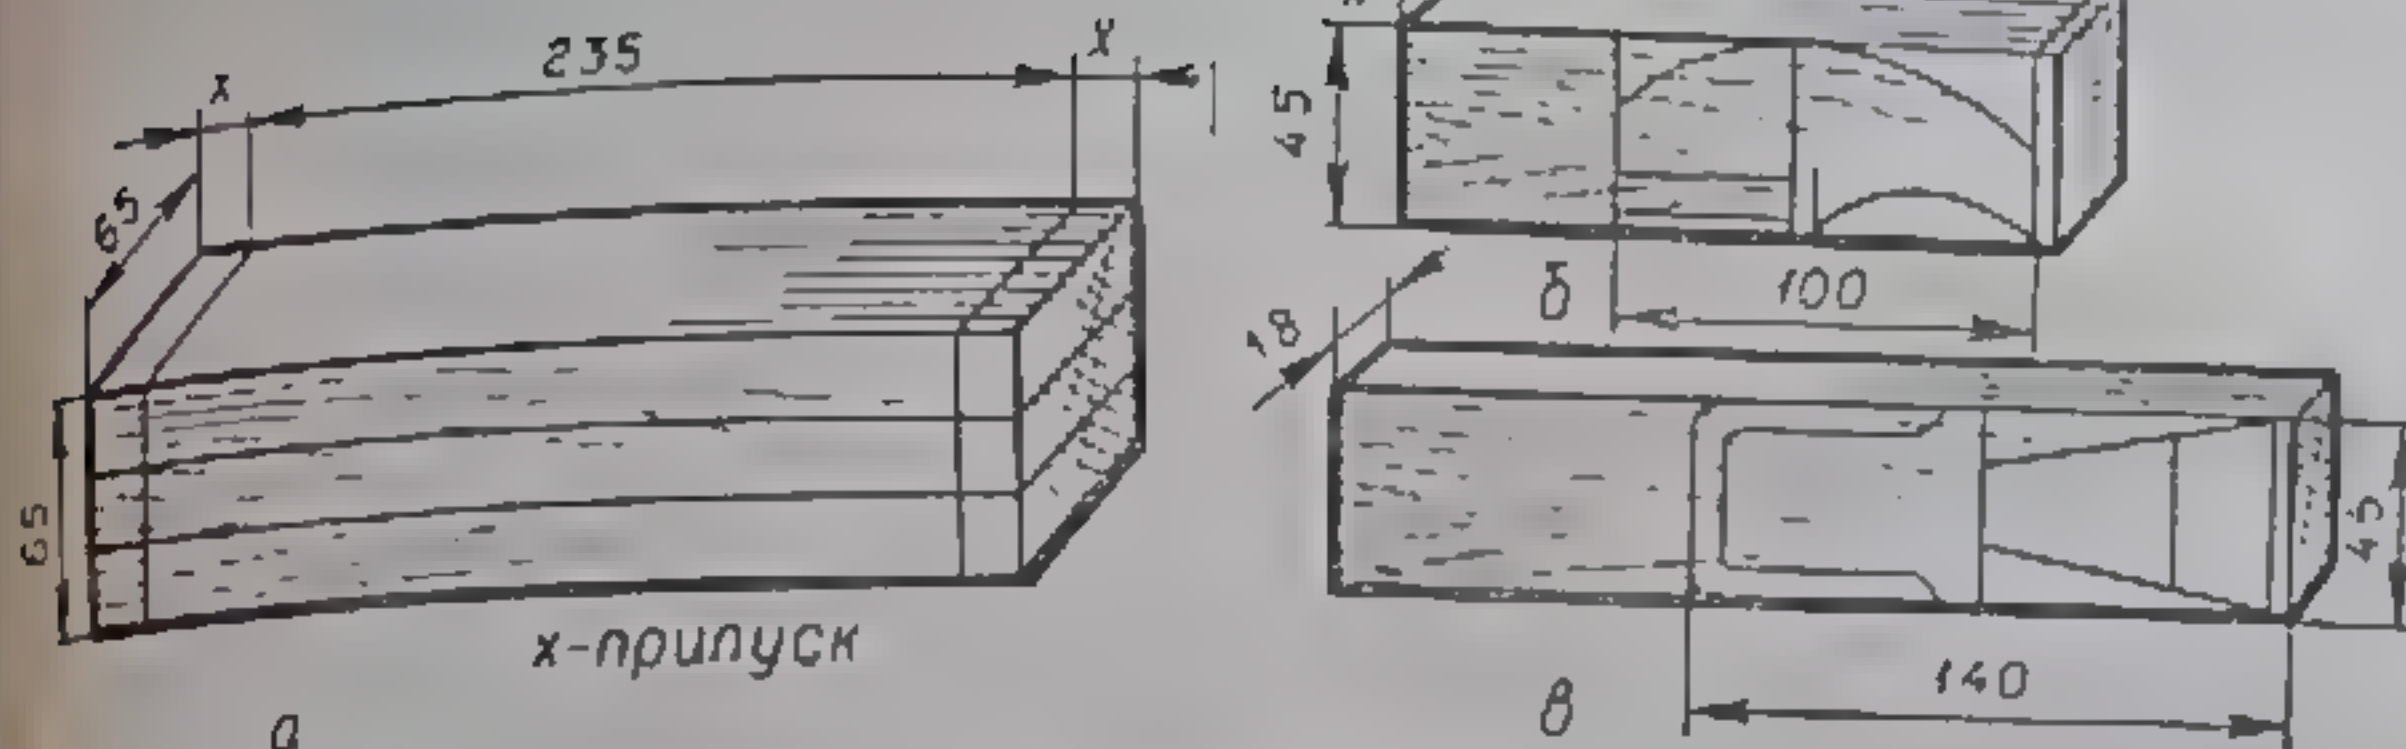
Заготовки для колодки (а), рожка (б), клина (в).
